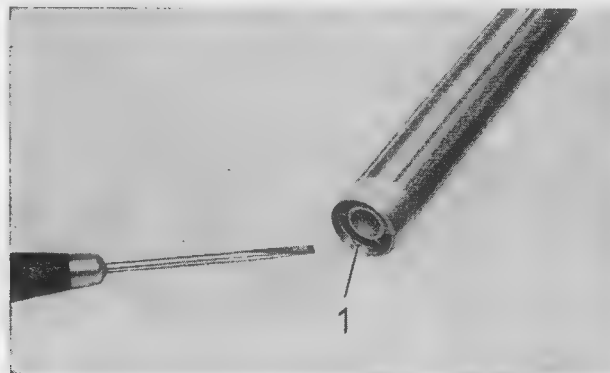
Rundring aus dem Führungsrohr herausdrücken
